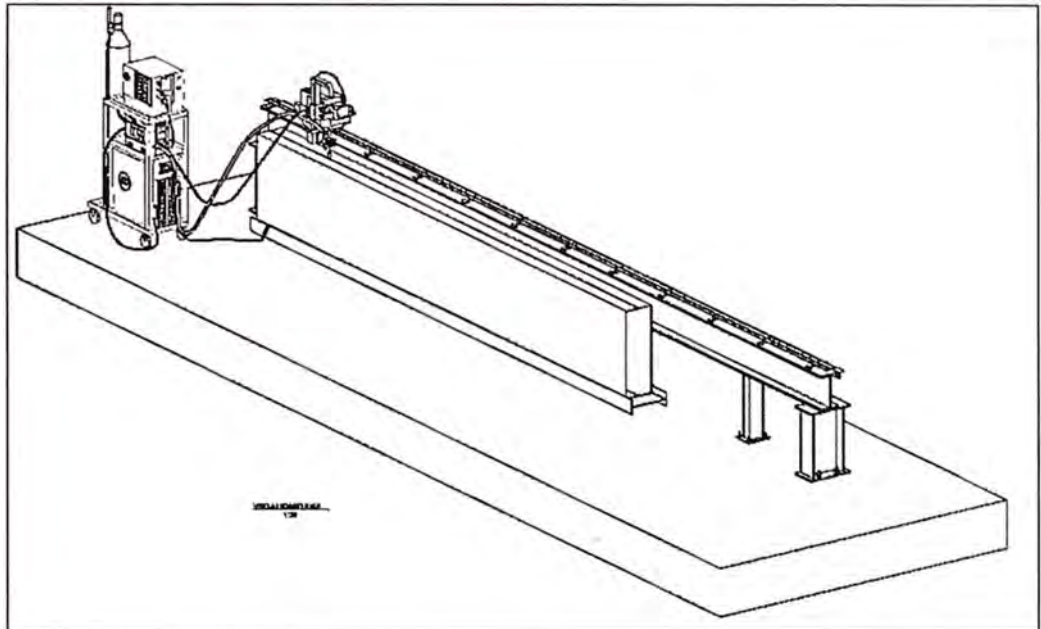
soldadura mecanizada de pórtico
